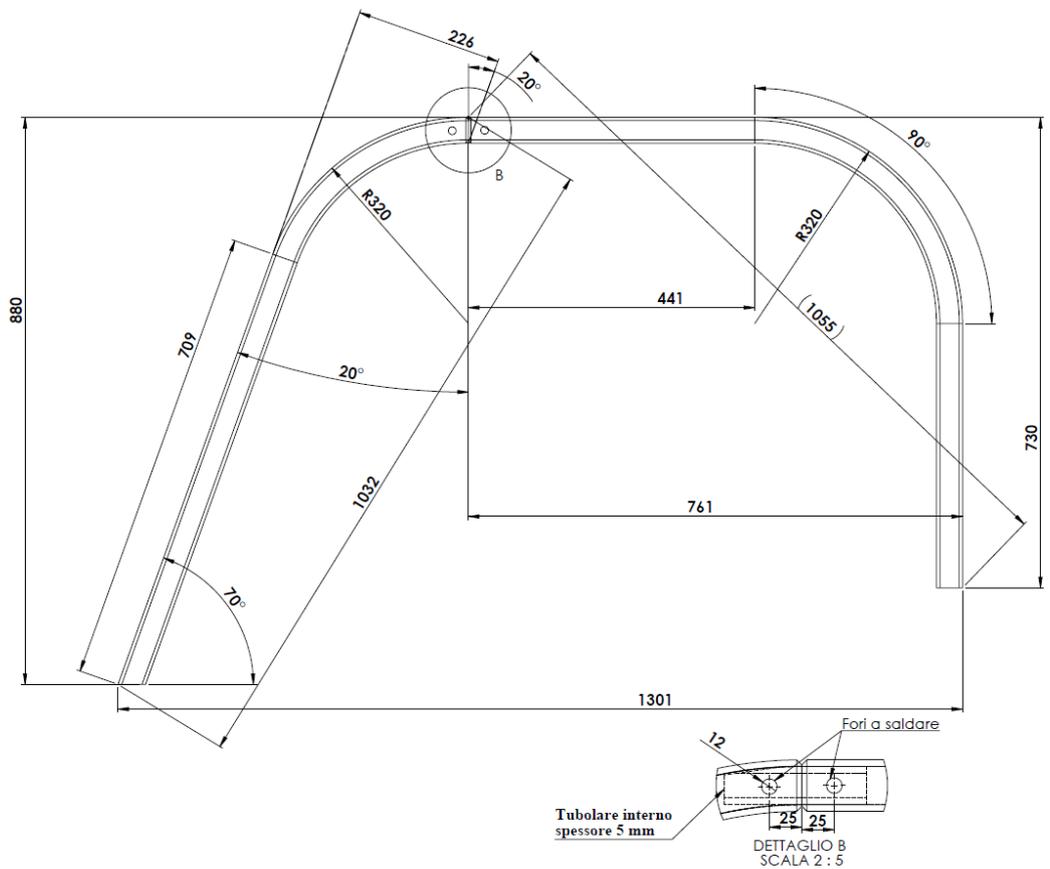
Profilo laterale del telaio di protezione, dettagli costruttivi e giunto a innesto saldato.
